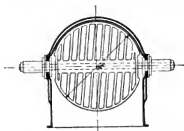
Geschweißtes doppelwandiges Kochgefäß mit Rührwerk.
